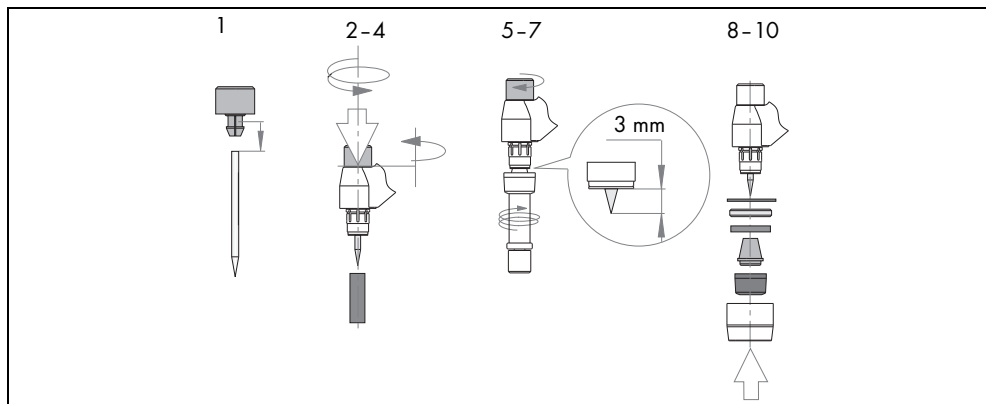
Opérations pour l'équipement du corps de torche ABIPLAS® WELD 250 CT20
